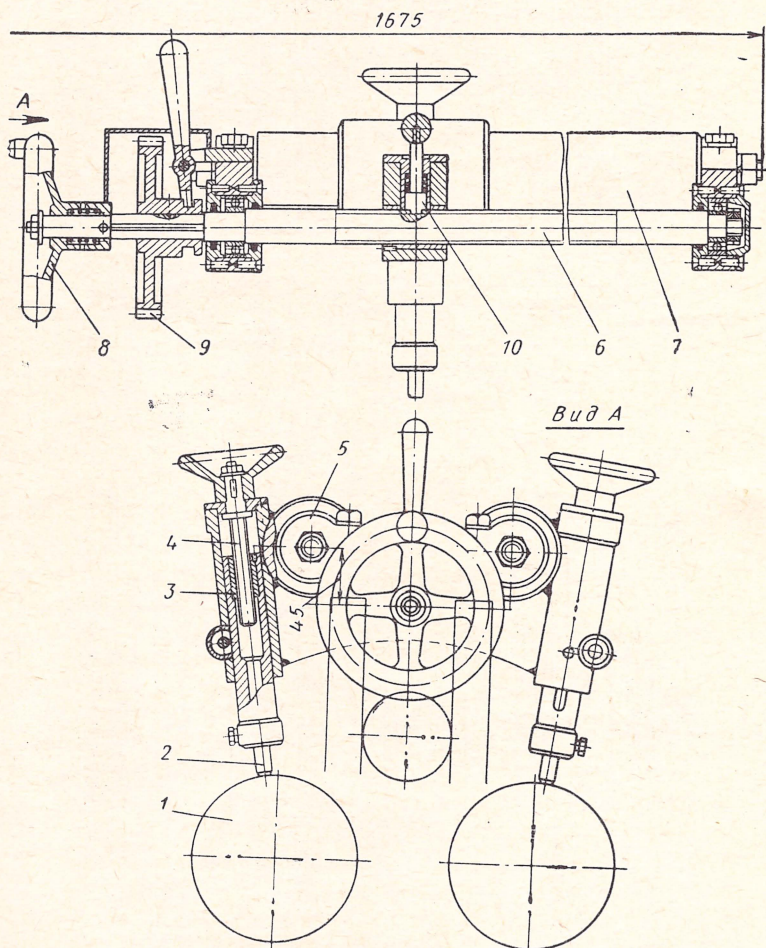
Приспособление для правки абразивных кругов на гратоснимательных станках
